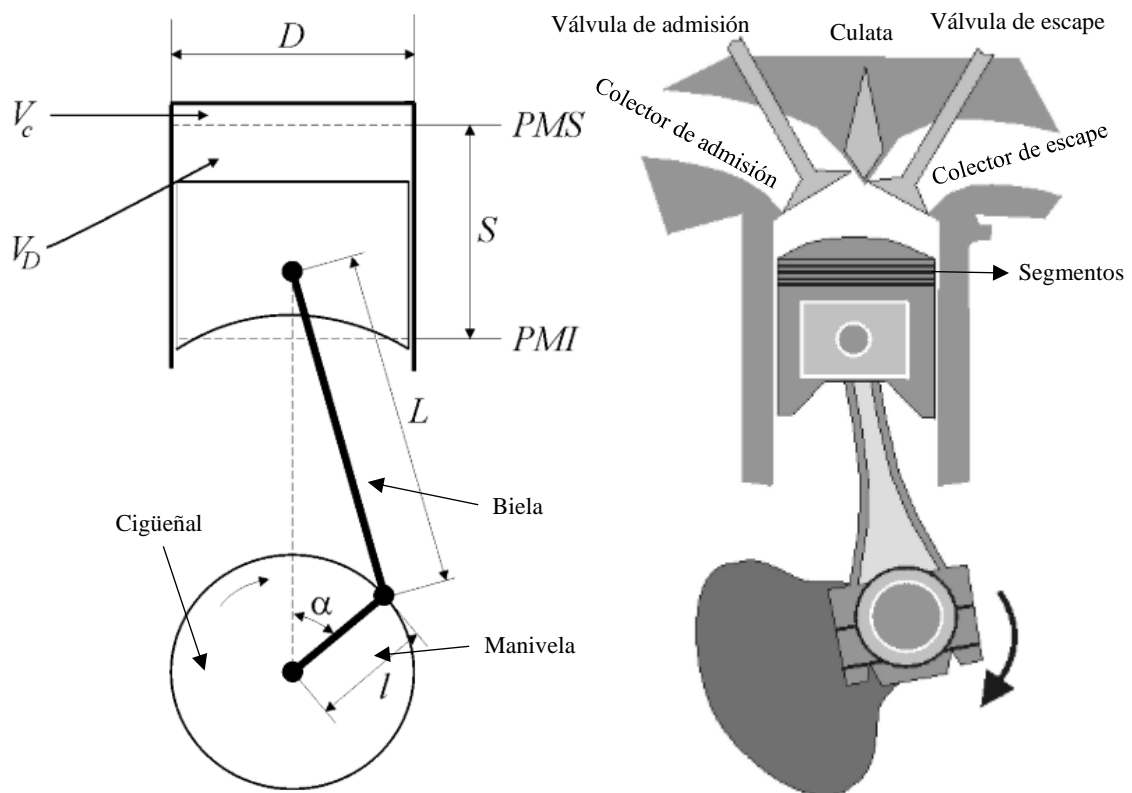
Esquemas de un motor de combustión interna alternativo [57].
